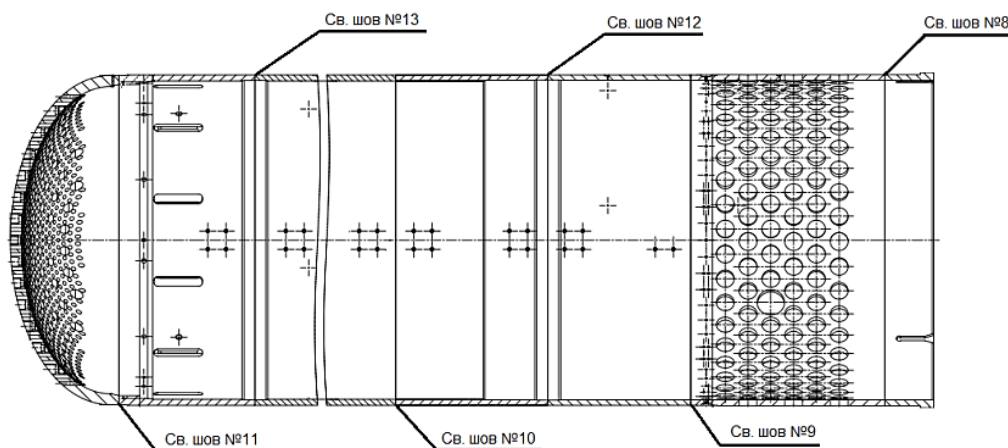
Сварные соединения Шахты внутрикорпусной, пригодные для контроля технологиями ФР
